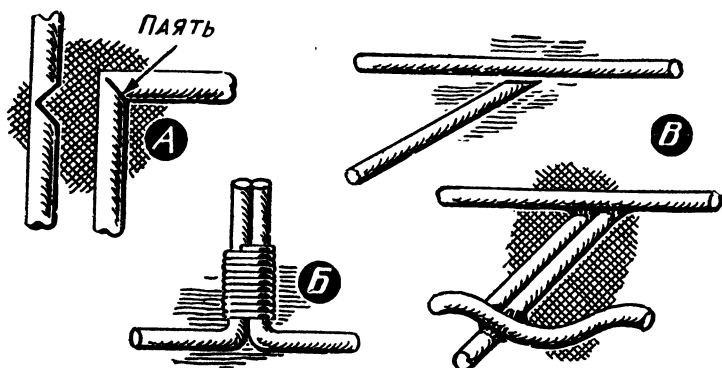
Обработка проволоки: А — перед изгибанием; Б — вариант пайки проволочных элементов; В — обработка концов проволоки перед соединением.
